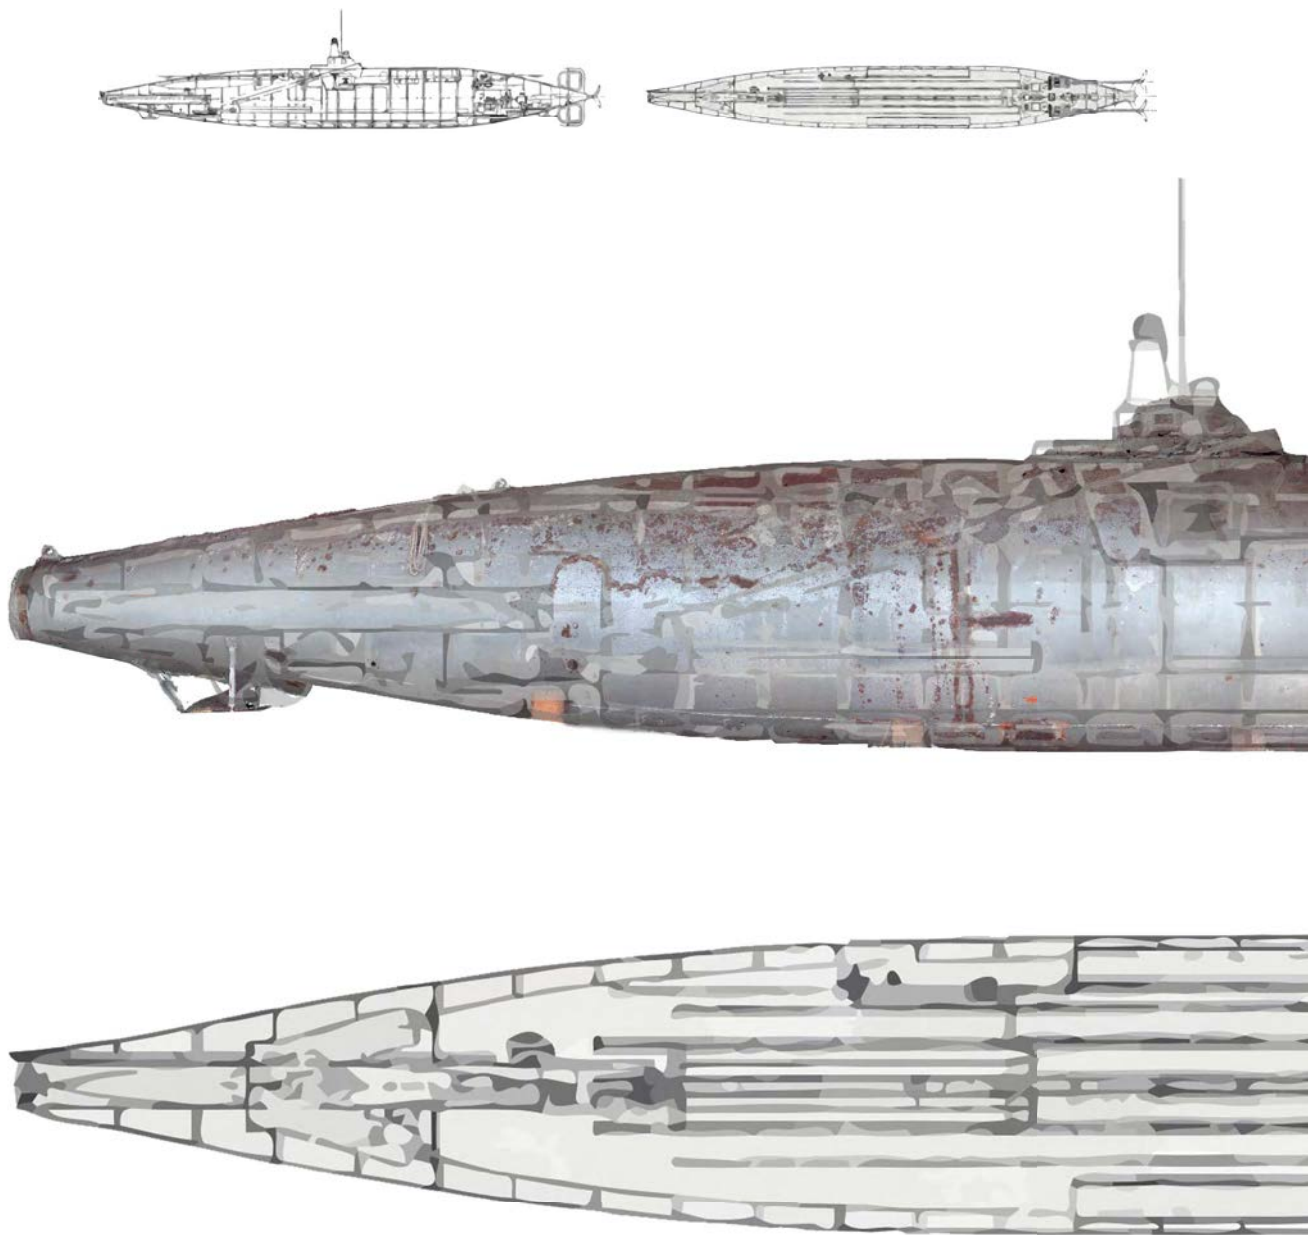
(superior). Planimetría submarino. Fuente: Archivo Base Naval Cartagena.
